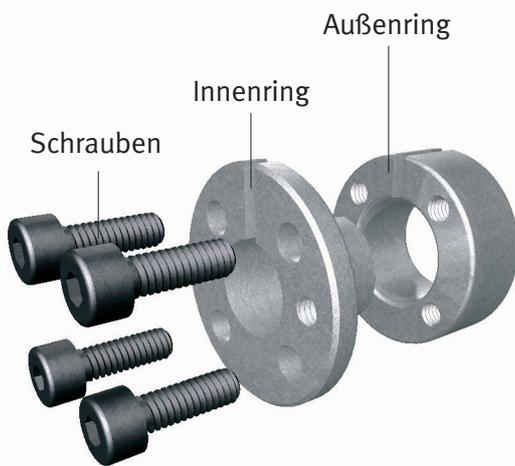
Befestigung einer Zahnriemenscheibe mit MAV 2061
